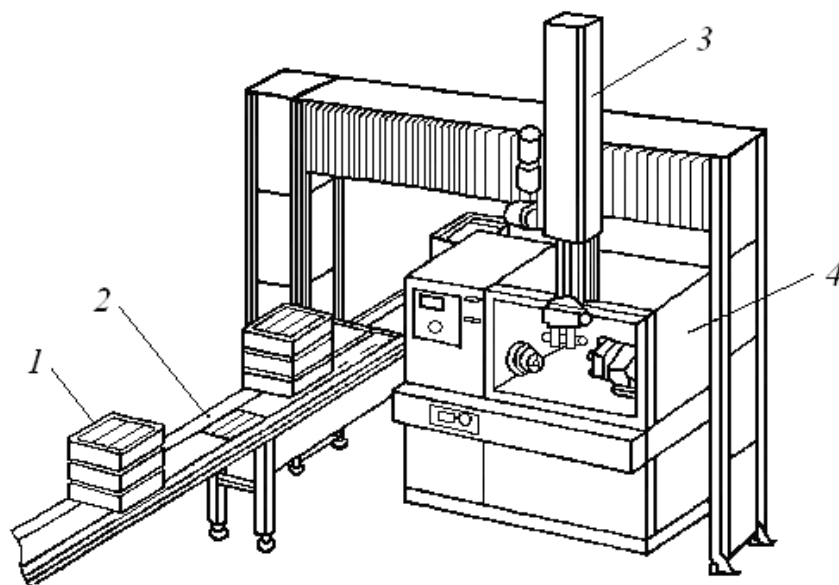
Общий вид РТК для обработки деталей типа «тела вращения» с обслуживающим роботом портального типа
